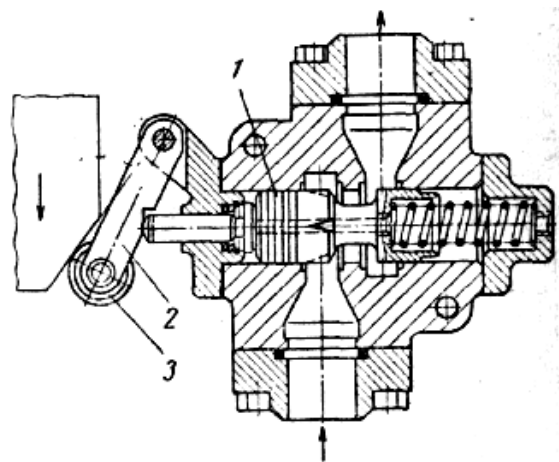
Дросельний керуючий пристрій: 1 – золотник; 2 – поворотний важіль; 3 – ролик
